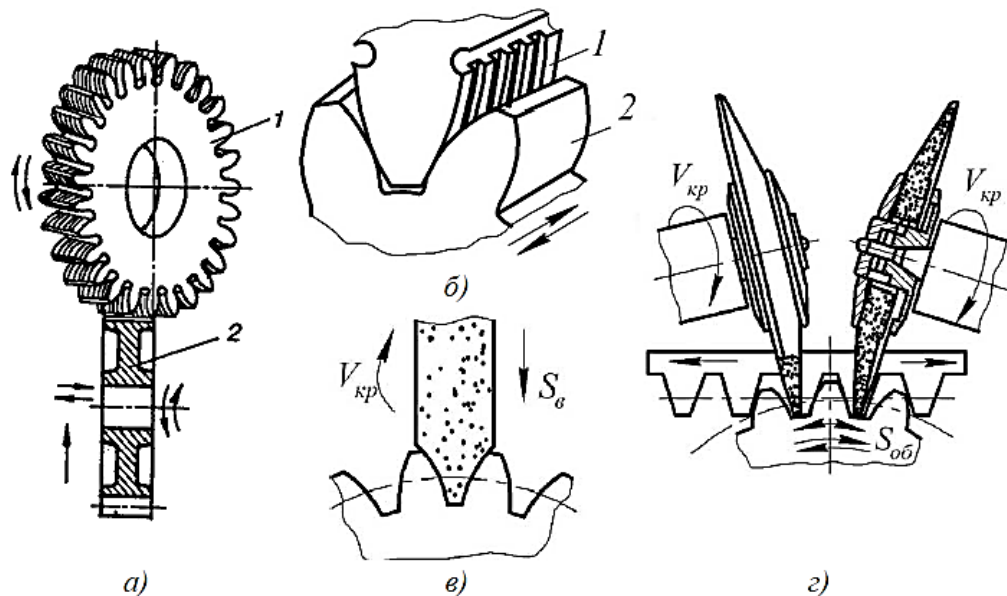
Схеми чистової обробки зубів зубчастих коліс
